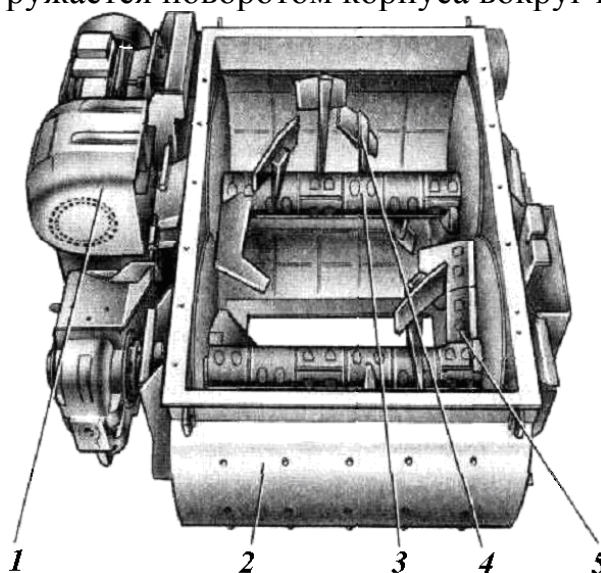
Двухвальный смеситель циклического действия с принудительным перемешиванием: 1 – привод валов; 2 – корпус; 3 – вал; 4 – лопасть; 5 – разгрузочный люк
